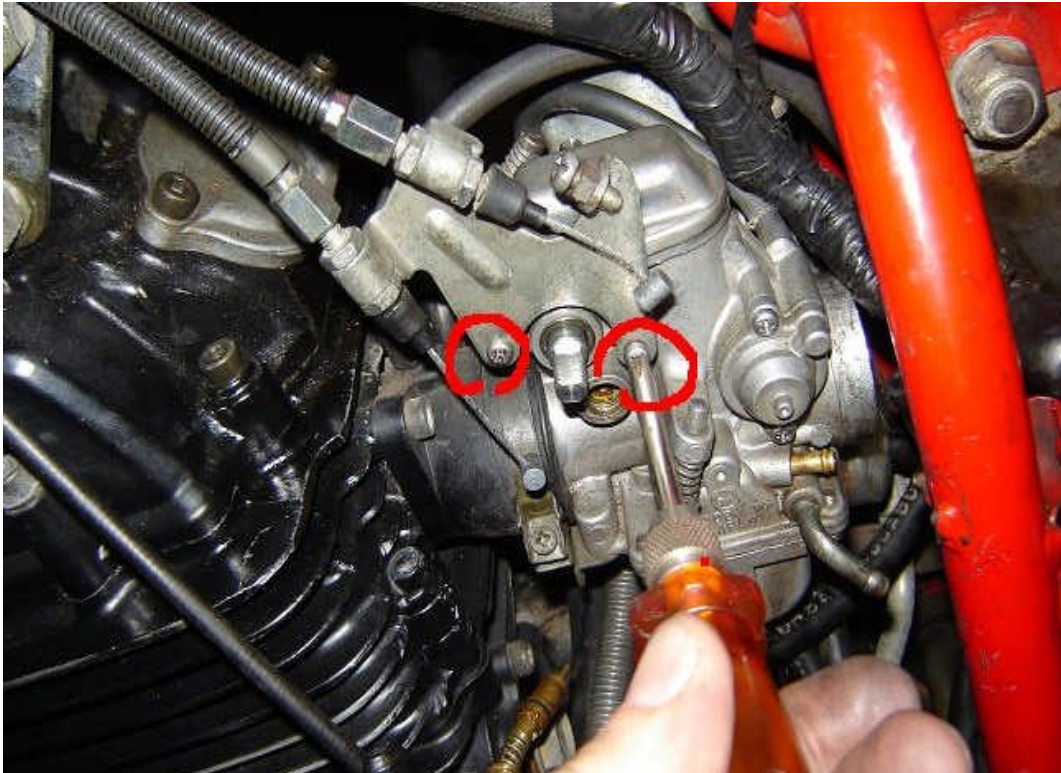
Schrauben des Betätigungsblechs lösen, Blech entfernen. Seilzüge weghängen.
